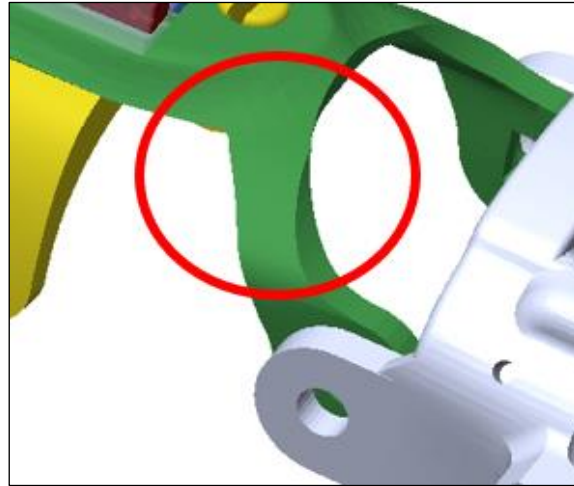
Rotura de las piezas de la unión entre Fixed Gauntlet y Rotating Gauntlet 1
